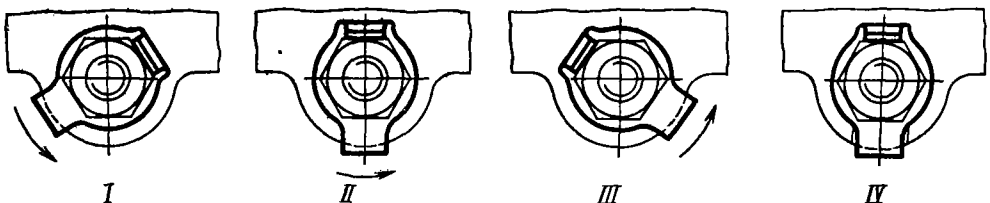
Установка стопорной шайбы на фланце с полукруглыми бобышками
